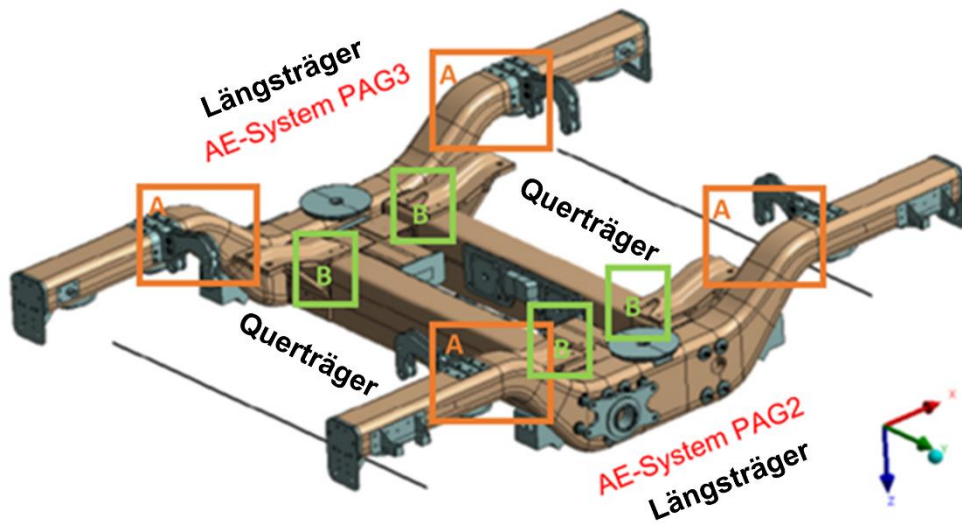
Instrumentierung der Schallemissionsmesstechnik auf dem Drehgestellrahmen, zwei AE-Messsysteme PAG2 und PAG3 (PAG - Gerätebezeichnungen), in jeder Zone A auf den Längsträgern 8 AE-Sensoren, in jeder Zone B auf den Querträgern 4 AE Sensoren.
